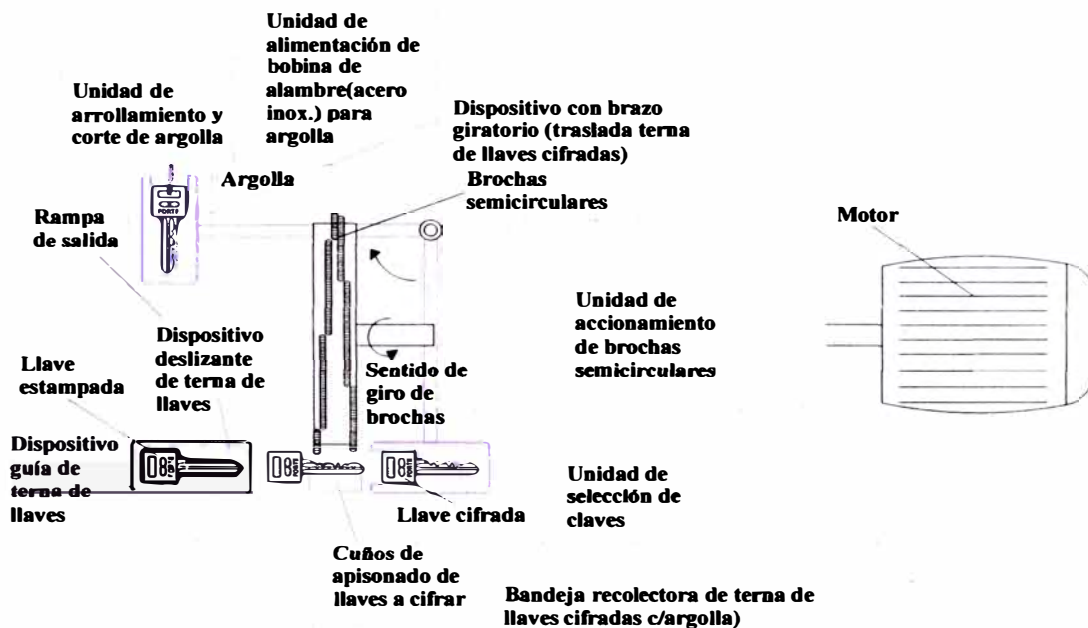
Vista en planta de la disposición de los dispositivos en la máquina de estampado
